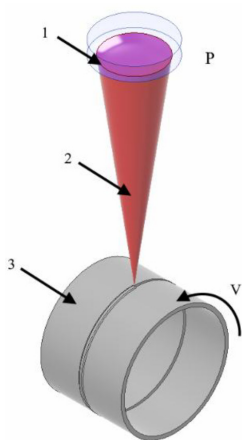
Схема лазерного зварювання, де 1 – лінза, 2 – лазерне випромінювання, 3 – деталі, що зварювалися
